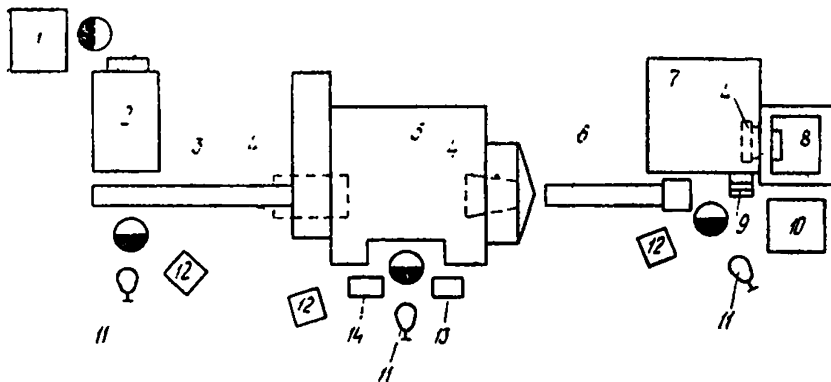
Агрегат кривошипного ковочно-штамповочного пресса усилием 1000—3000 тс.:
